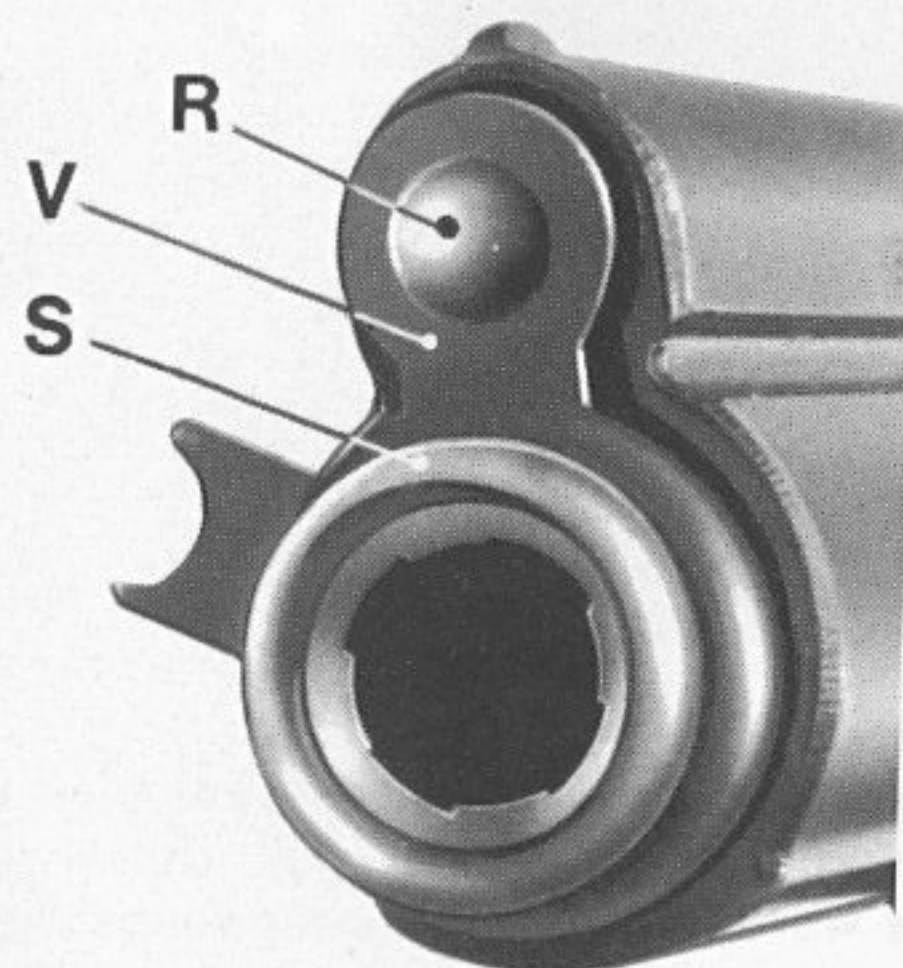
Zur Demontage drückt man das Federstützlager R nach hinten und schraubt die Laufmutter S ab.
